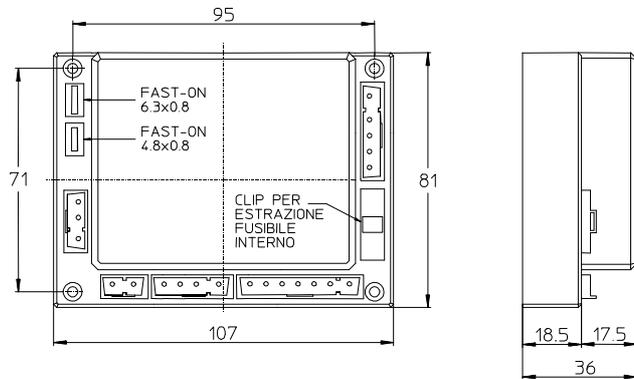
Dimensioni di ingombro dell'apparecchiatura
